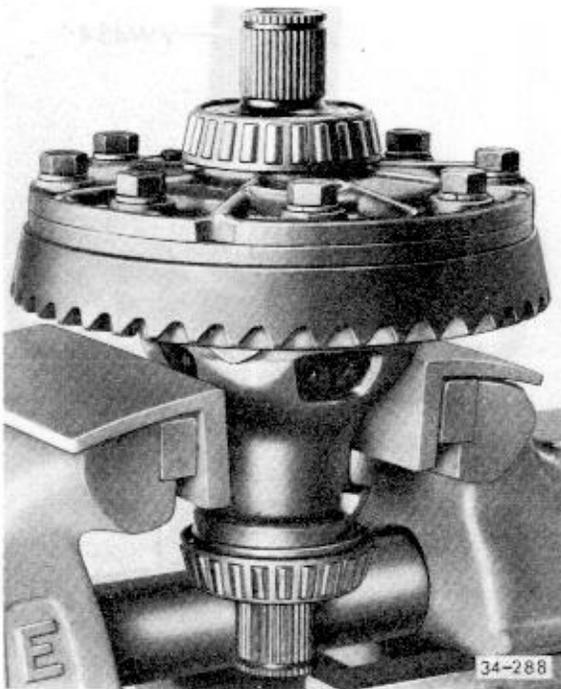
Ausgleichgetriebe in den Schraubstock spannen
